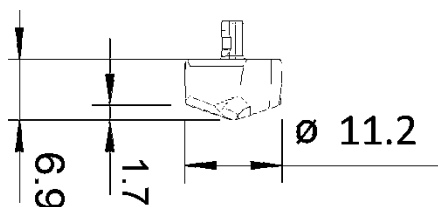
Сменная головка сверла CoroDrill®870 870-1100-8-ММ
